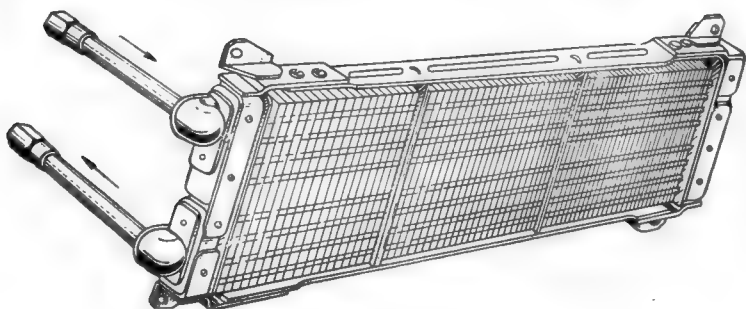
Масляный радиатор двигателя ГАЗ-51
